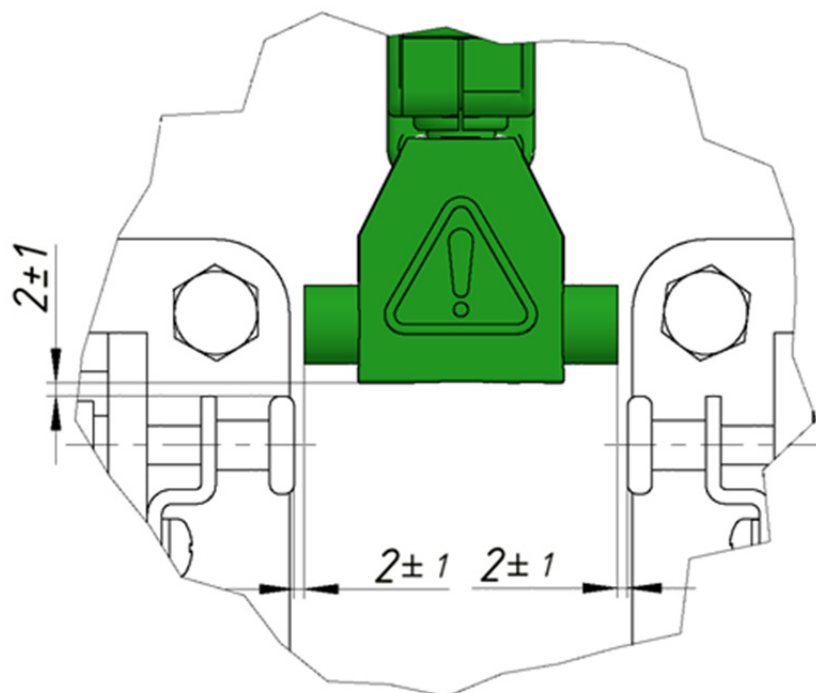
Установка блокиратора со сдвоенными разъединителями
